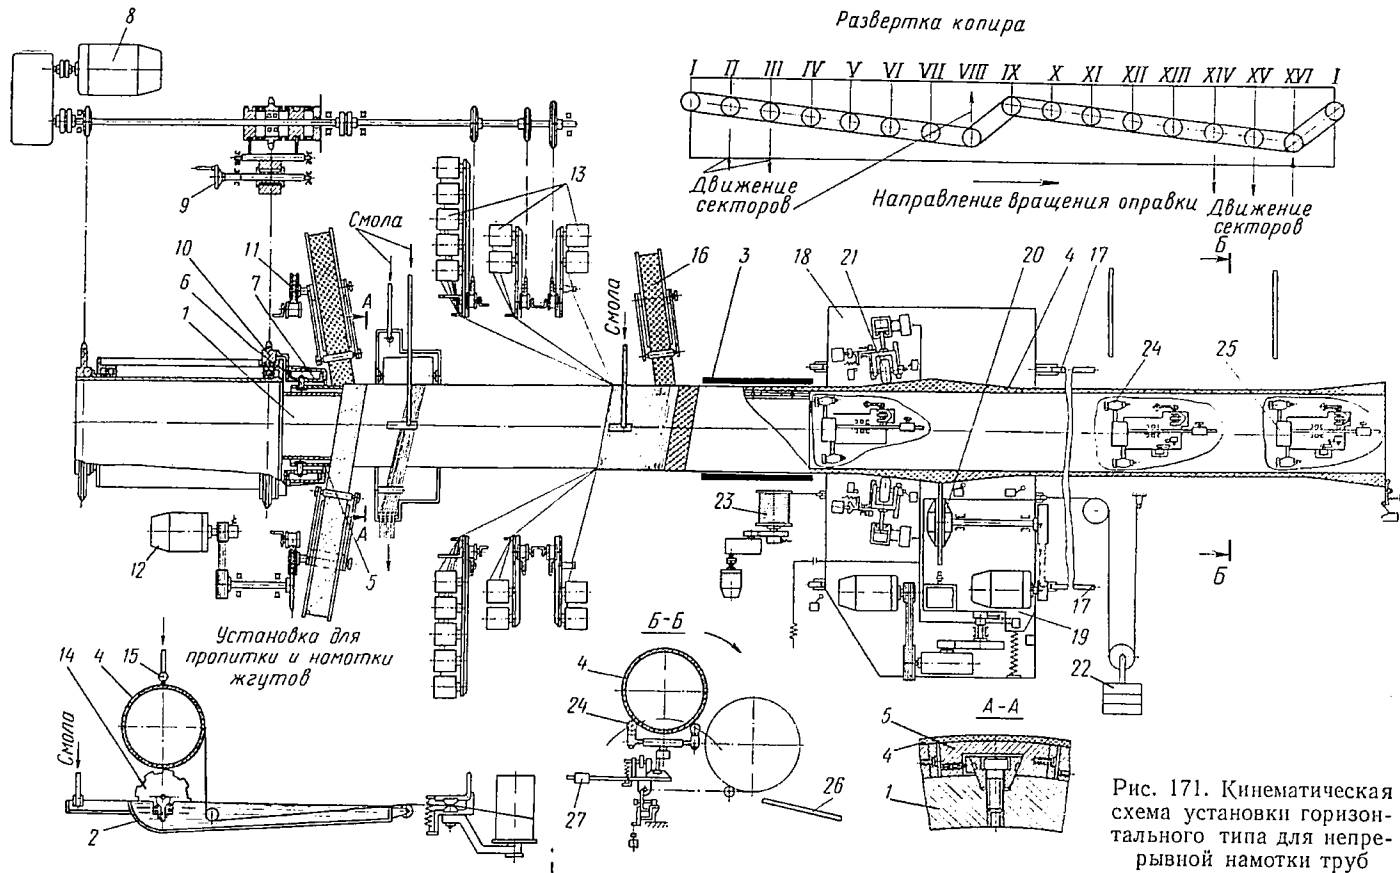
Кинематическая схема установки горизонтального типа для непрерывной намотки труб
